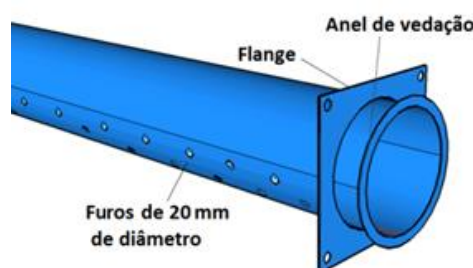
Duto-eixo, mostrando o posicionamento do anel e flange de conexão ao ventilador.
